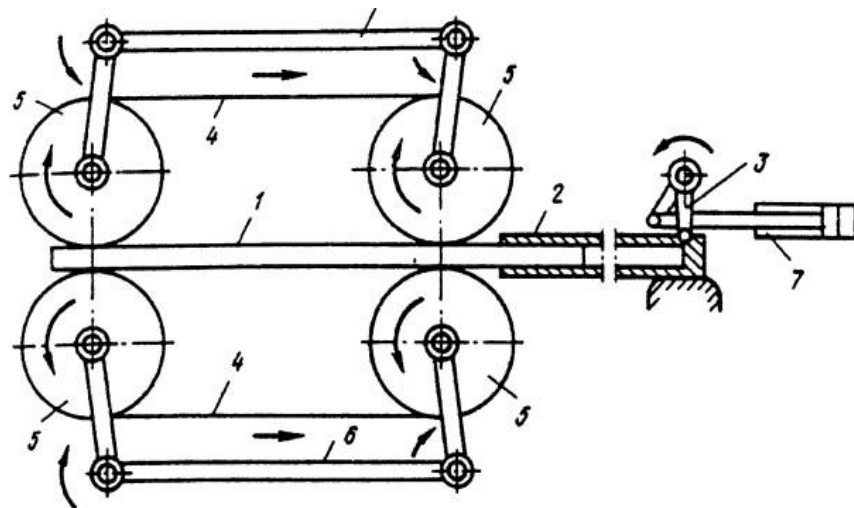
Фрикційний пристрій для виймання оправки з труби:
